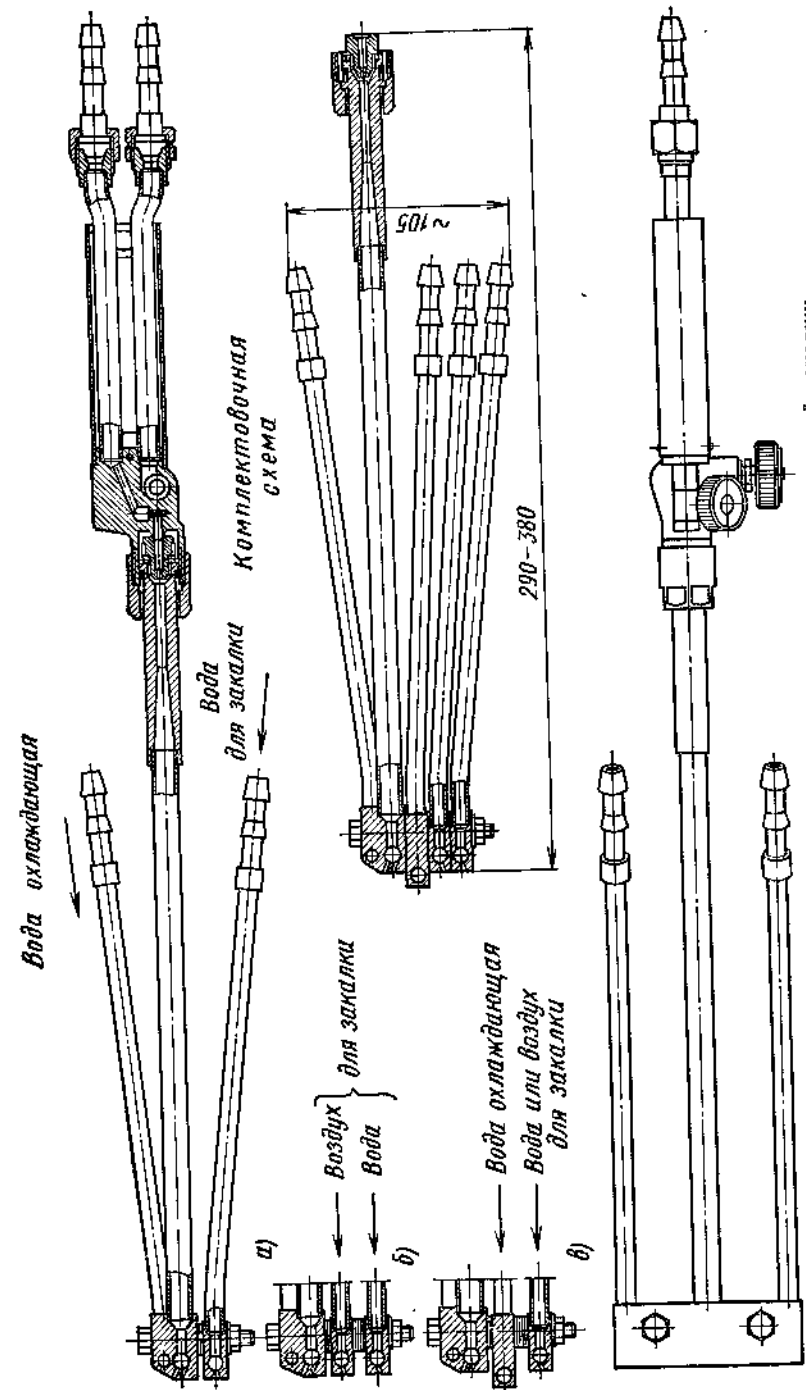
Схемы сборки наконечника НАЗ для поверхностной закалки: а — на мартенсит, б и в — на троостит и сорбит
